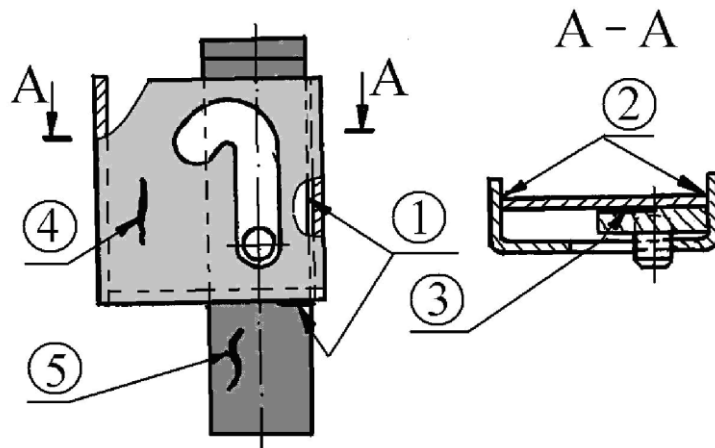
Нижній запірний механізм торцевої двері напіввагона
